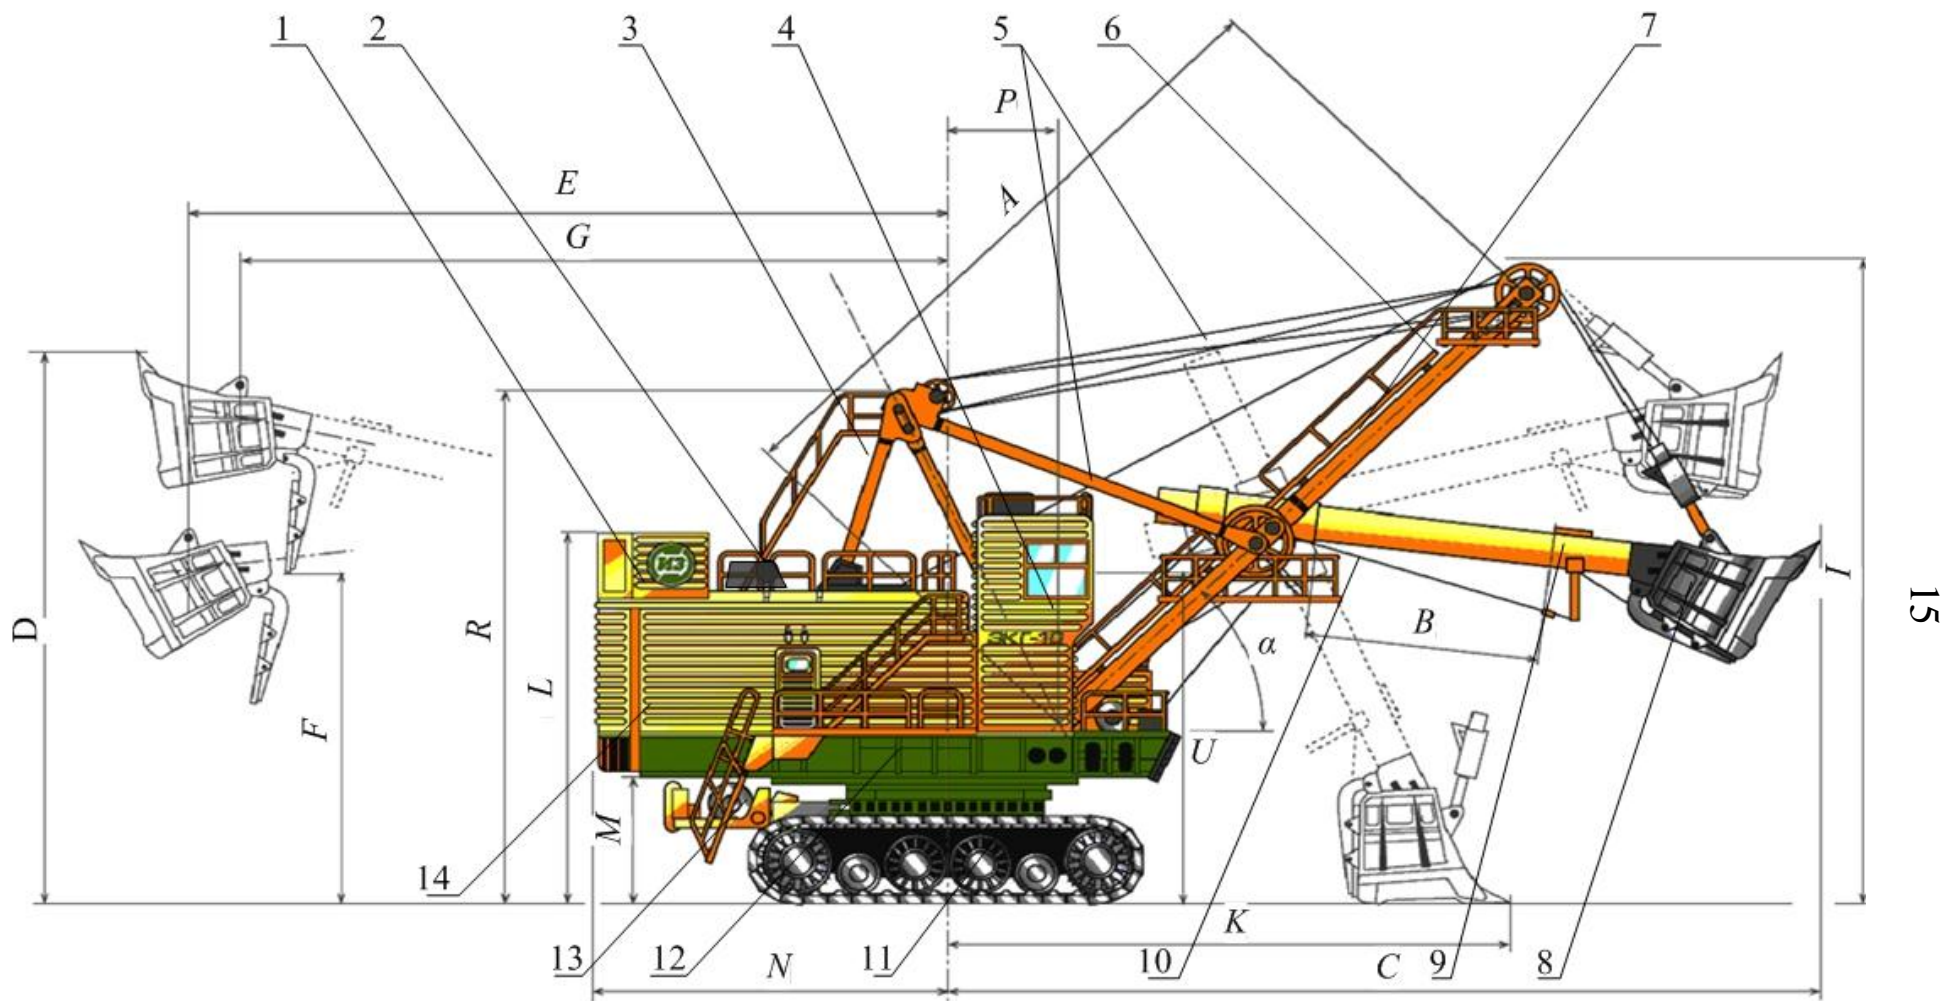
Общий вид экскаватора и схема рабочих размеров.
